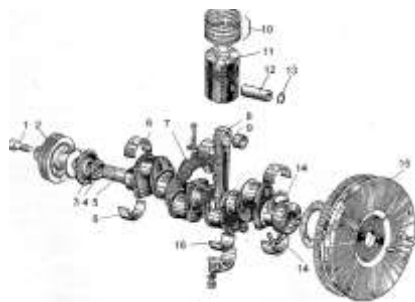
Деталі кривошипно-шатунного механізму
